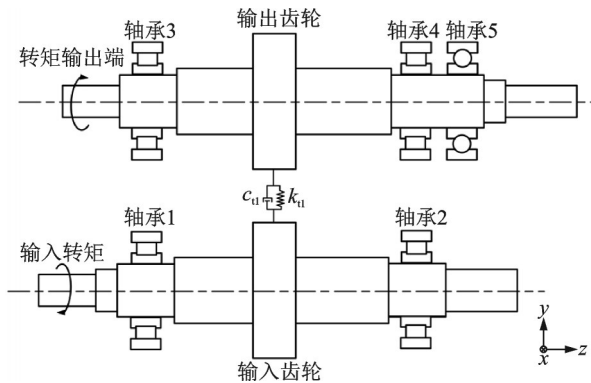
轴承-轴-齿轮传动系统多自由度动力学模型
